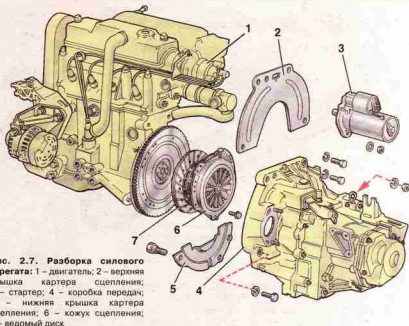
Разборка силового агрегата: 1 – двигатель; 2 – верхняя крышка картера сцепления; 3 – стартер; 4 – коробка передач; 5 – нижняя крышка картера сцепления; 6 – кожух сцепления; 7 – ведомый диск
